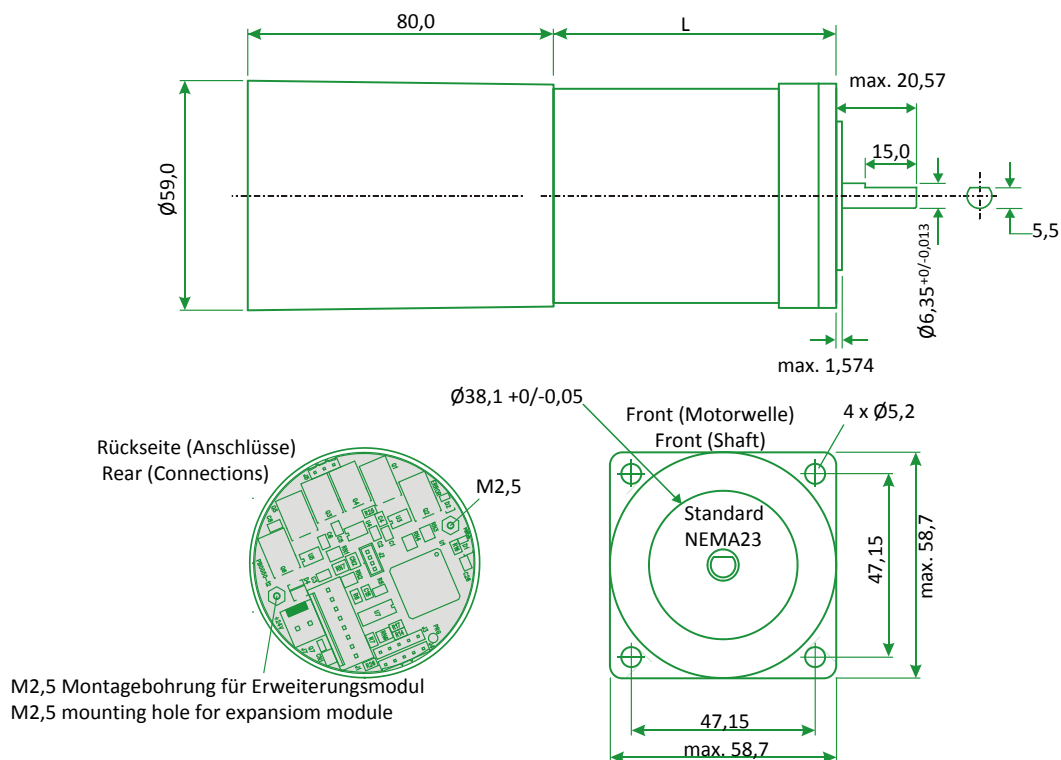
MAC050 - MAC141 Zeichnung ohne Erweiterungsmodul, Dimensionen [mm]
